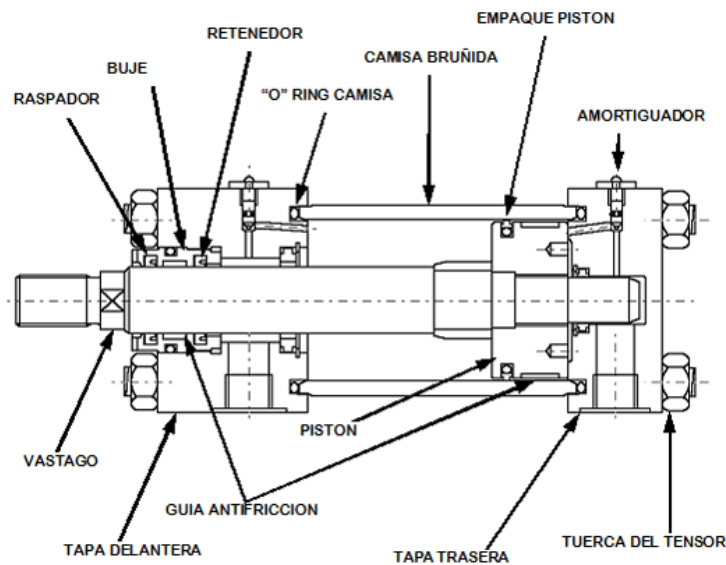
29: Partes de un cilindro de doble efecto.
